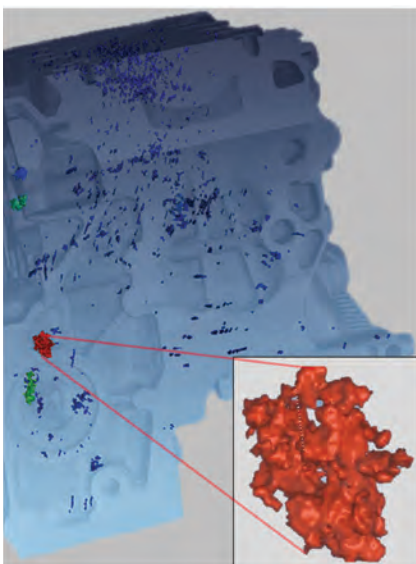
Porosität in einem gegossenen Al-Zylinderkurbelgehäuse [18].
